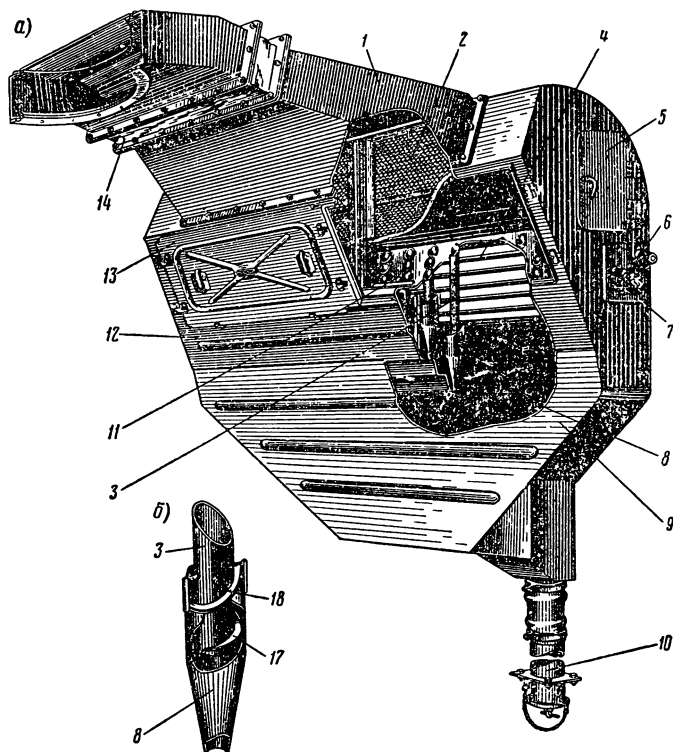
Общий вид воздушного фильтра (обозначения см. на рис. 142):
